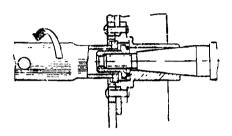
Ослабление затяжки контргайки крепления маховика ключом
